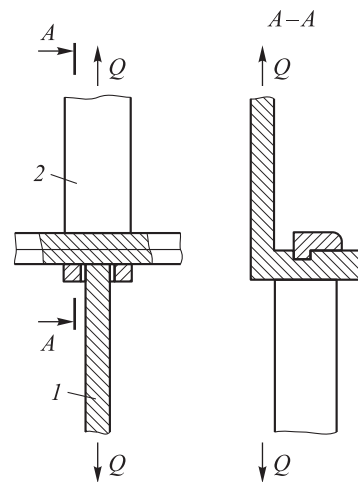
Схема испытания на прочность сварного соединения лопасть — накладка
